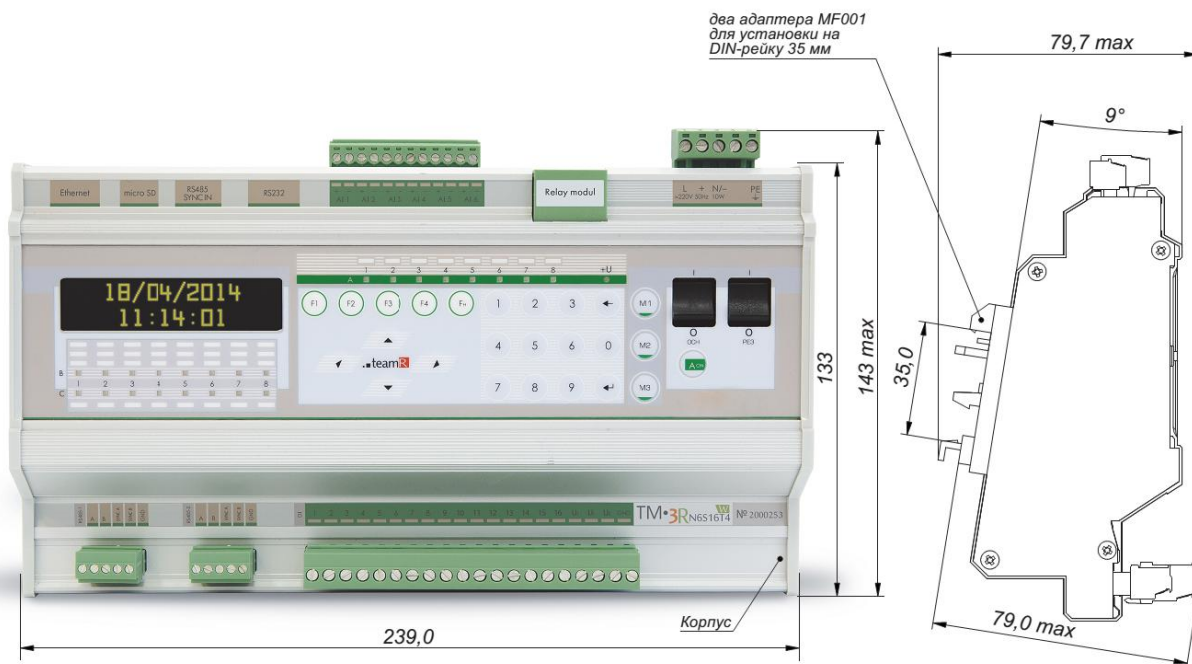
Габаритный чертеж устройства «ТМ3R»
